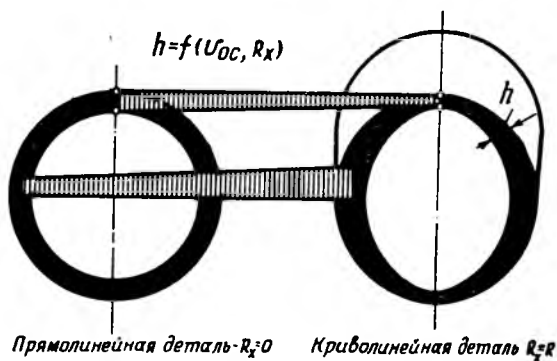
Характер неравномерности шлифования криволинейных деталей на маятниковых станках
